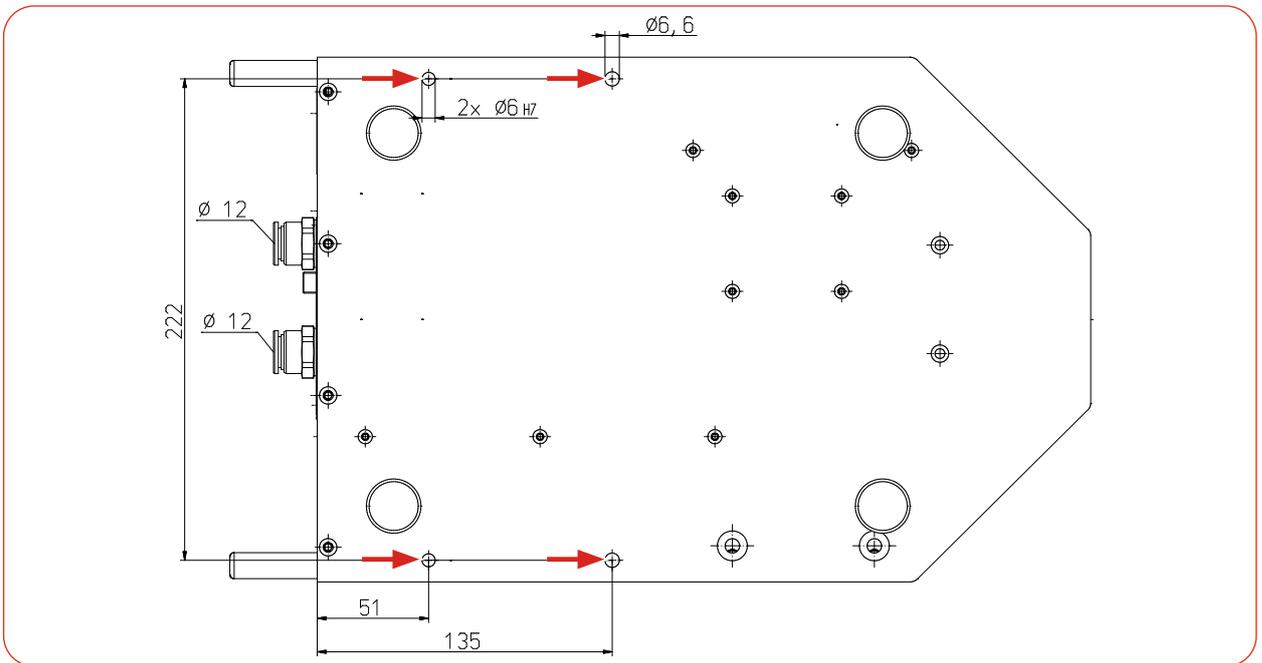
Passbohrungen und Befestigungsbohrung, Ansicht von unten
